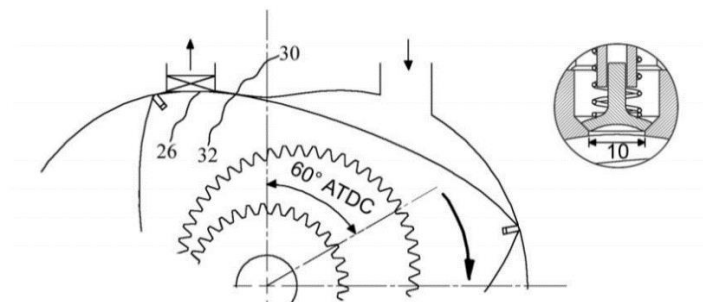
Вложение боковой поверхности ротора с отверстием корпуса в конце такта выпуска; со вставным видом выходного клапана (три установлены поперечно).
